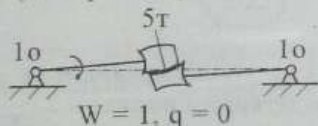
Зубчастий механізм із точковим зачепленням Новикова
